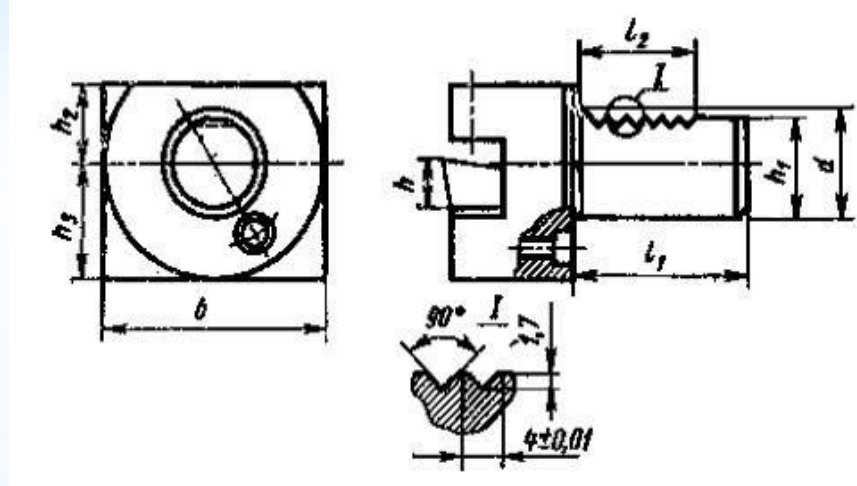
Общий вид резцового блока с рифлёным цилиндрическим хвостовиком
